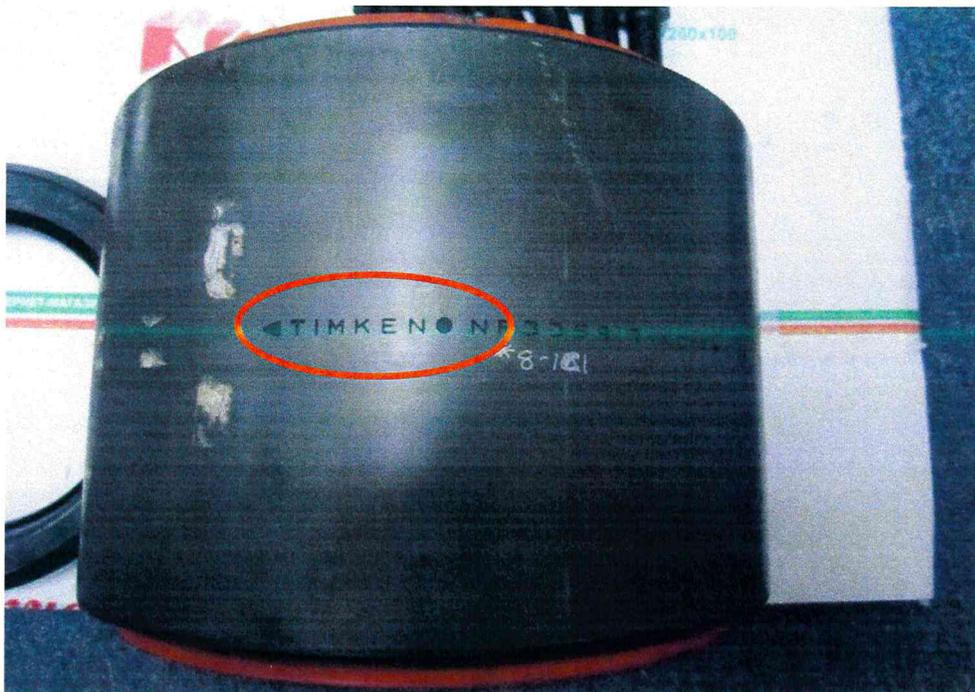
Маркировка наружного кольца кассетного подшипника торговой марки TIMKEN.
